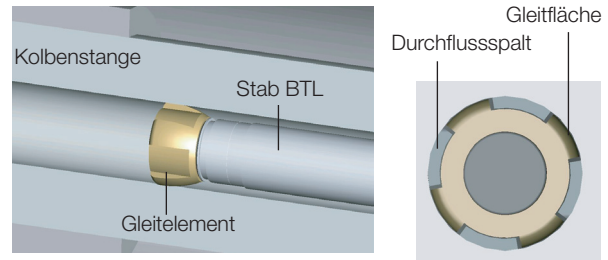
Detailansicht und Draufsicht Gleitelement
